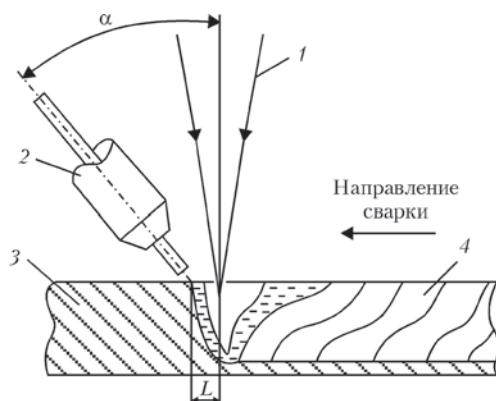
Схема гибридной лазерно-дуговой сварки: 1 — сфокусированное лазерное излучение; 2 — плавящийся электрод; 3 — свариваемый образец; 4 — шов
